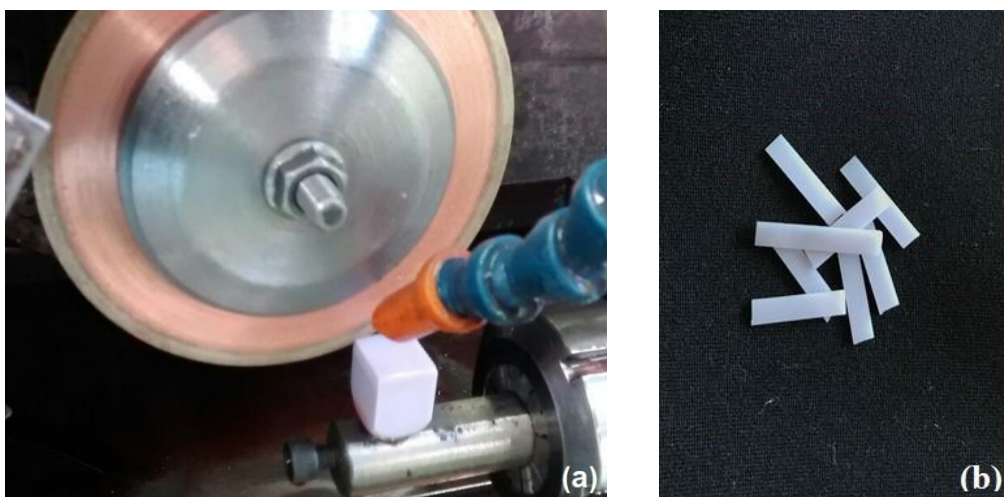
Bloco pré-fabricado IPS e.max CAD utilizado no sistema CAD/CAM
